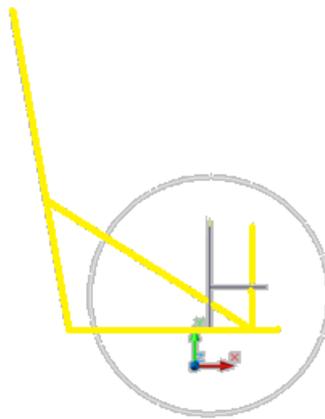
Vista lateral del diseño de la parte frontal del vehículo³³
